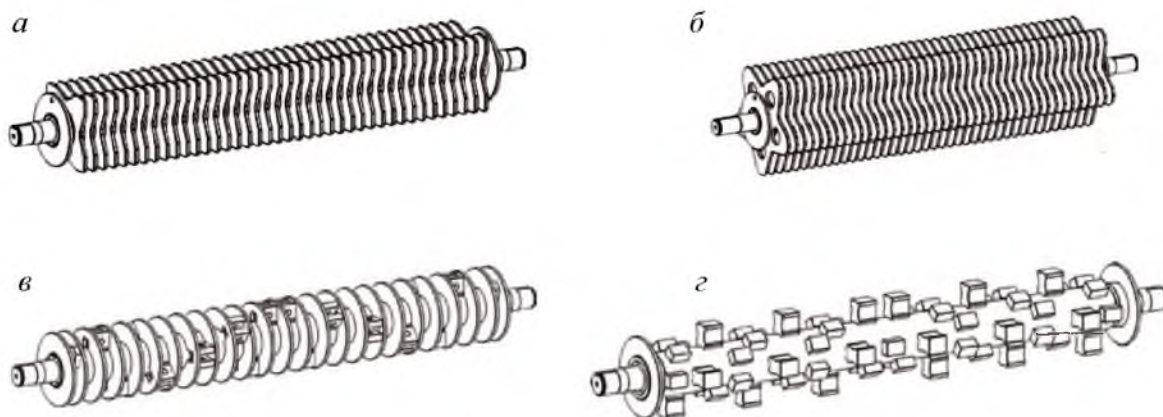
Барабаны ковшовой дробилки: а и б – 4- и 5-лепестковые соответственно; в – с заменяемыми ножами; г – с жестко закрепленными дробящими элементами
